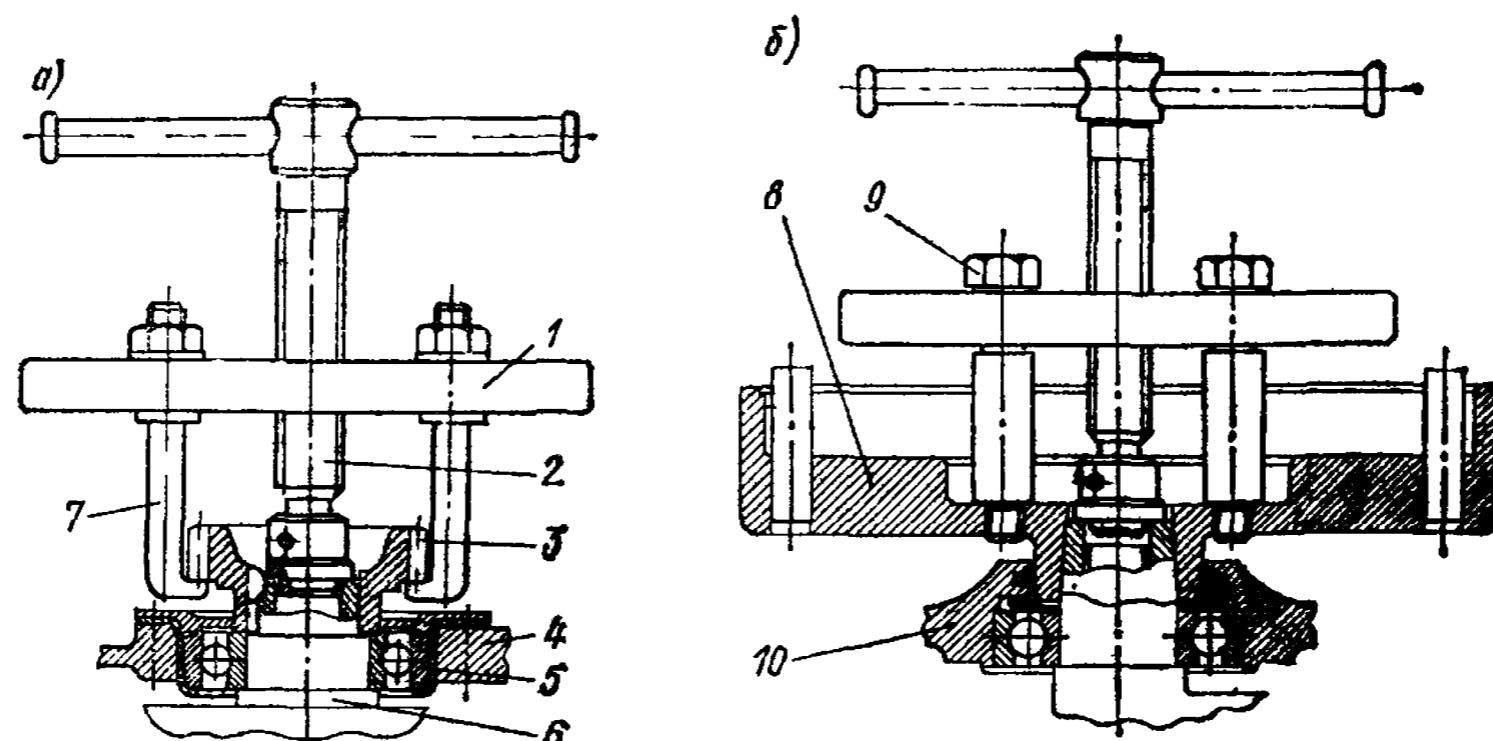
Универсальный съемник для зубчатого колеса и маховика: а — снятие зубчатого колеса распределения; б — снятие маховика;
